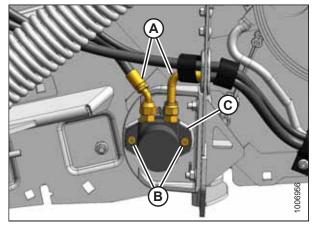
Moteur hydraulique arrière - Côté gauche
